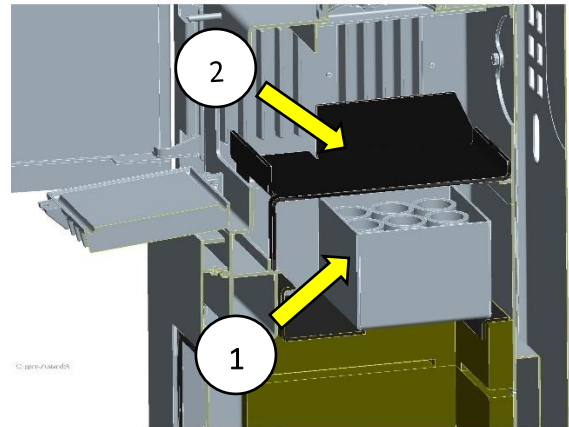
position technique de filtre HiClean® wodtke (HCF02)
